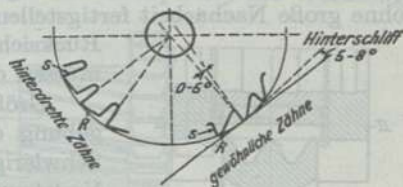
Gewöhnliche und hinterdrehte Fräserzähne.
